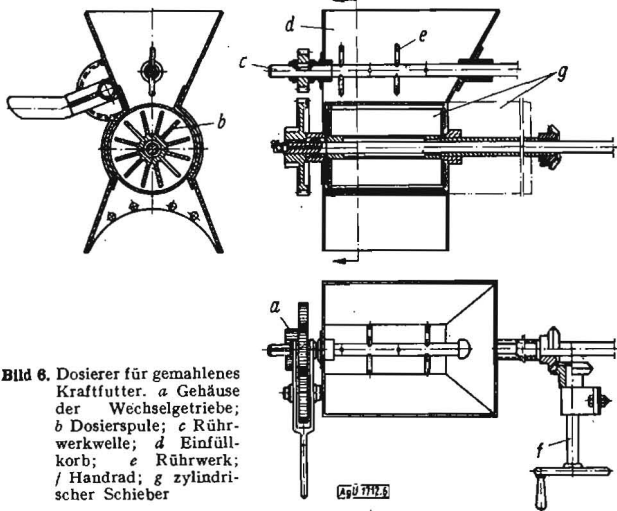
Dosierer für gemahlene Kraftfutter. a Gehäuse der Wechselgetriebe; b Dosierspule; c Rührwerkswelle; d Einfüllkorb; e Rührwerk; f Handrad; g zylindrischer Schieber
